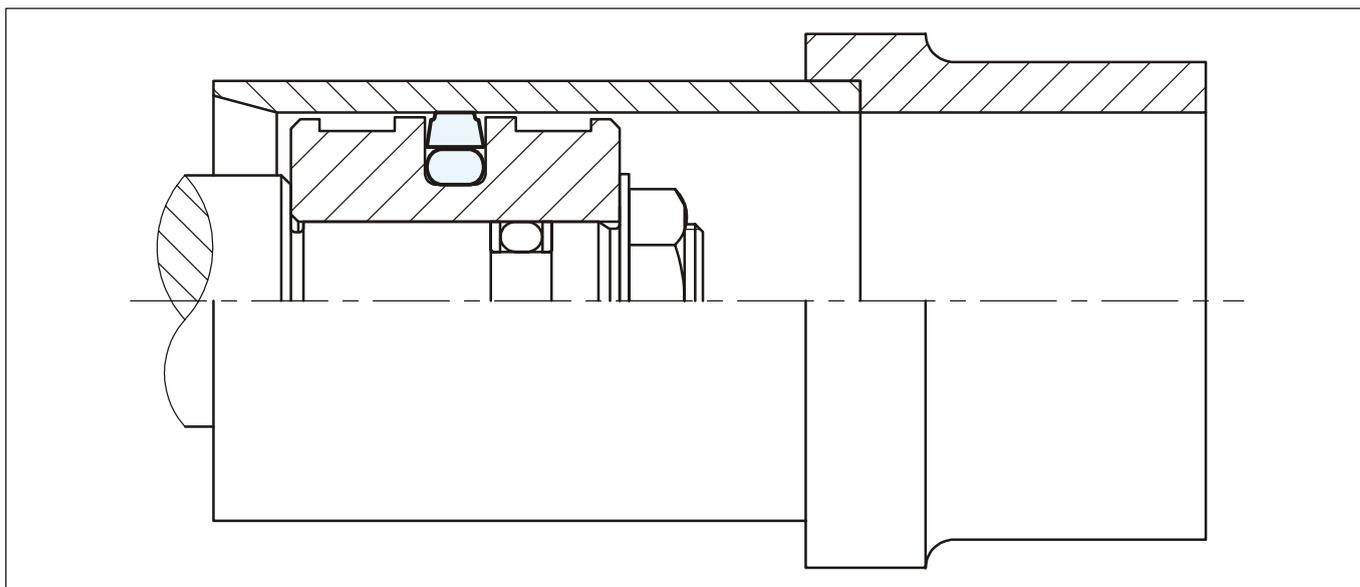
Калибровка уплотнительного элемента калибрующей втулкой
